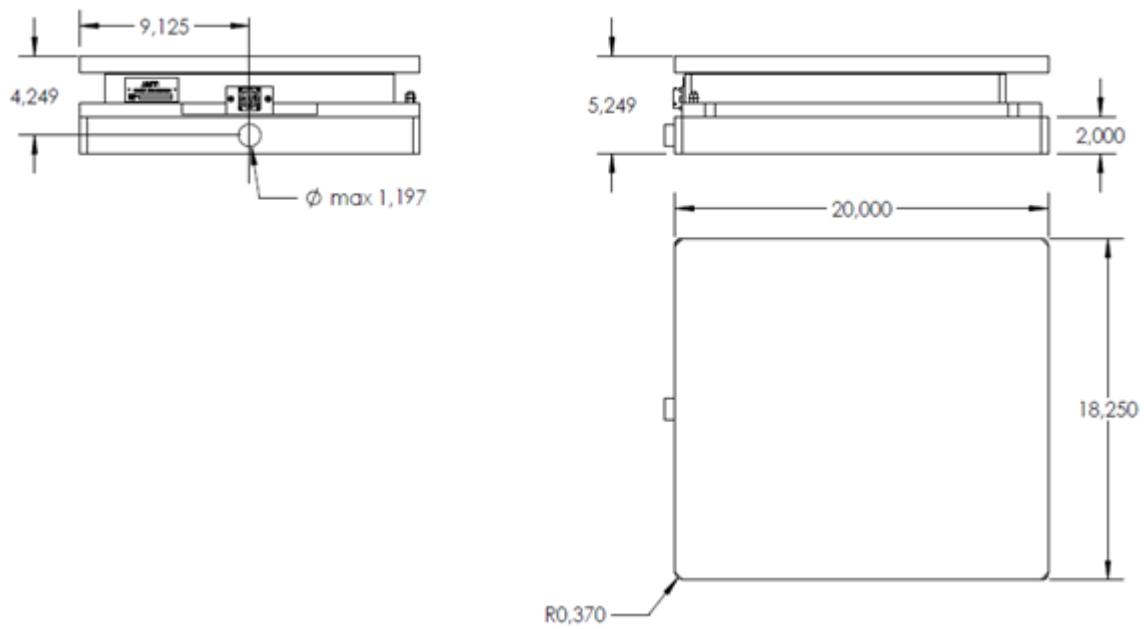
Dimensions d'une plateforme de forces avec sa base
